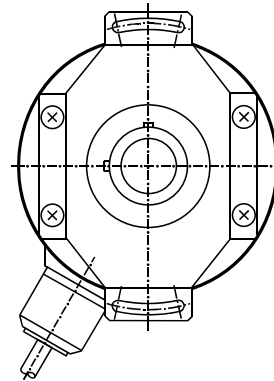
, Befestigungsbügel für Hohlwellendrehgeber
